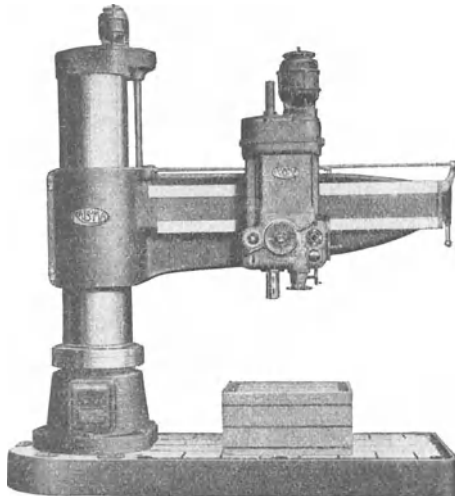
Schwenkbohrmaschine. (Raboma, Berlin.)
